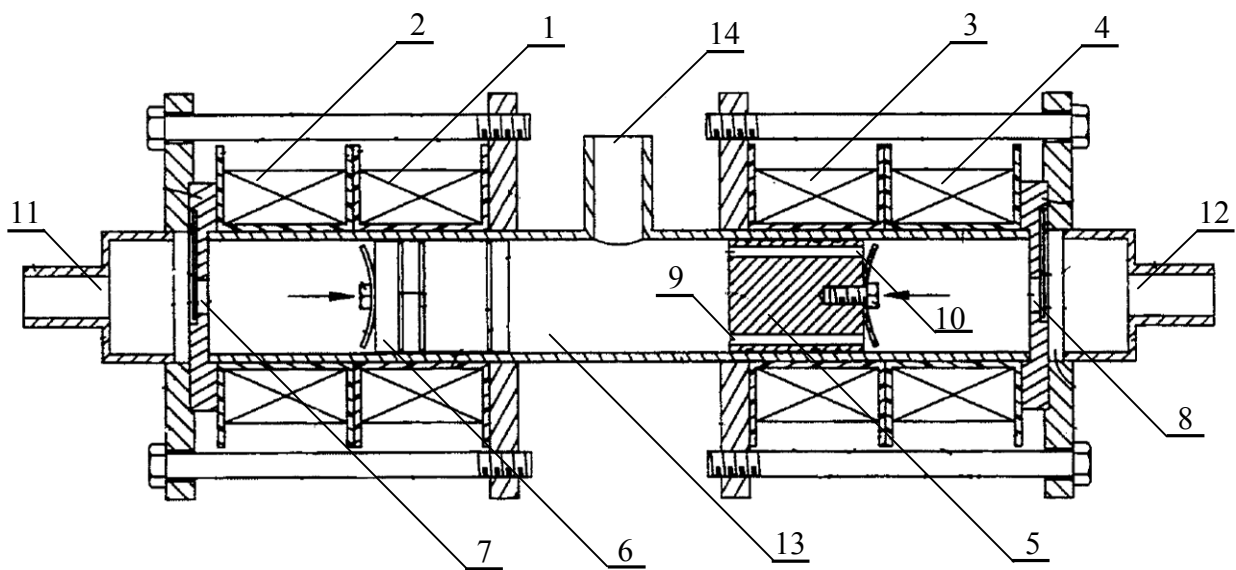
Двухсторонний электромагнитный компрессор с
